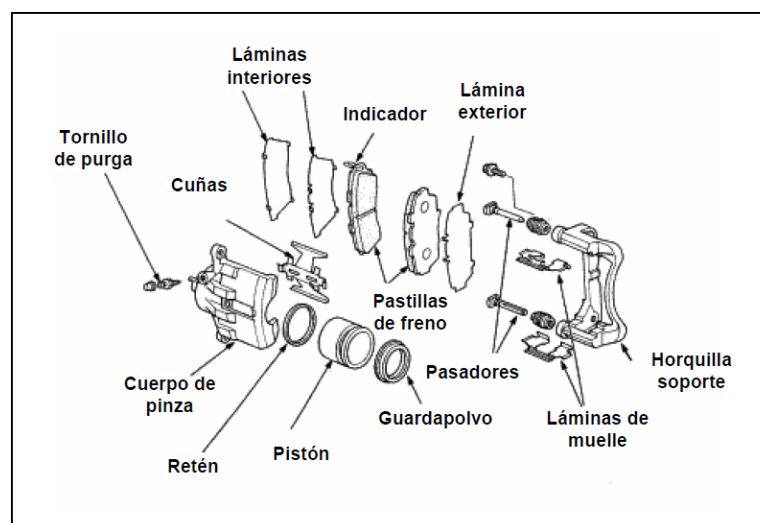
Plano de despiece del conjunto pinza flotante-pastillas.
